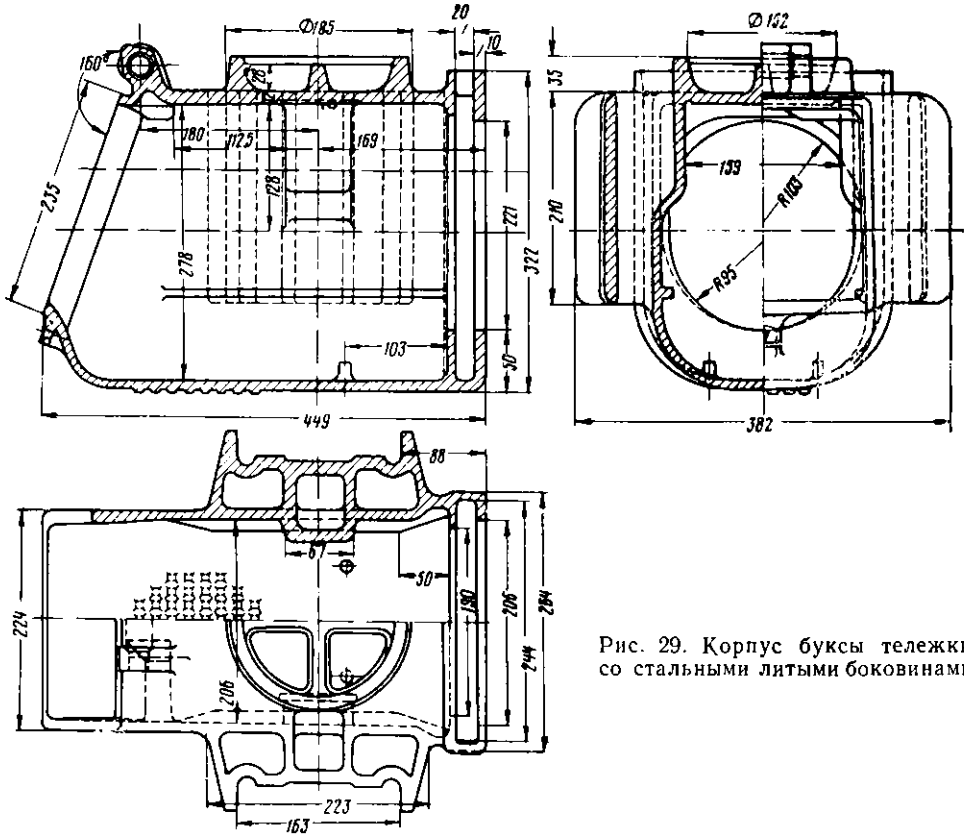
Корпус буксы тележки со стальными литыми боковинами
